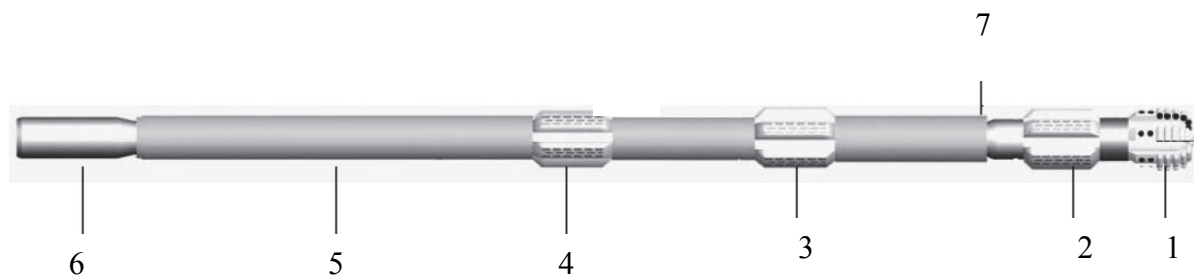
Компоновка *DART*: 1 – долото; 2 – скребок; 3 – несоосный стабилизатор; 4 – соосный стабилизатор; 5 – эксцентрик; 6 – сердечник; 7 – механизм ориентации торца долота
